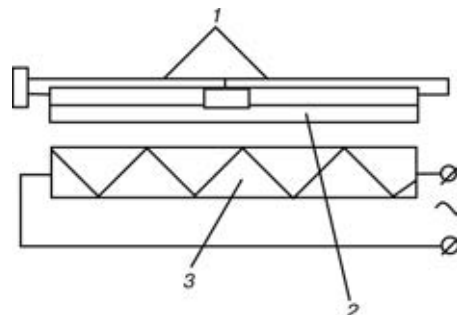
Схема устройства для пайки образцов: 1 — стыковые образцы из меди; 2 — плита из алюминия; 3 — нагреватель
